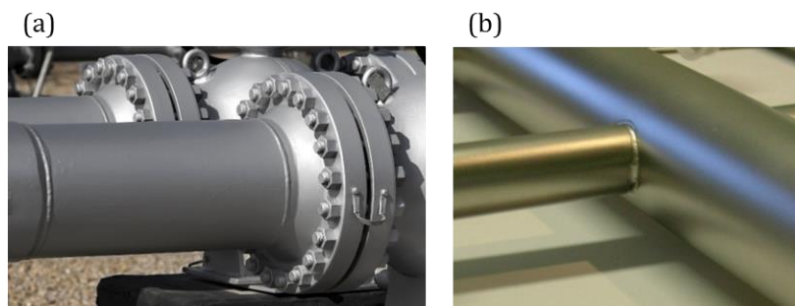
Exemple d'une bride (a) et d'un piquage soudé (b) sur des canalisations
